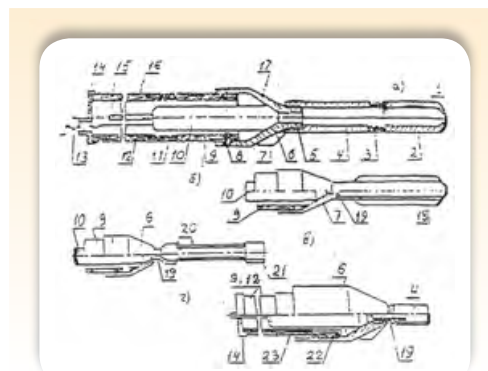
Схемы агрегата и его элементов для разрушения и замены ветхих трубопроводов новыми из полимерных трубных модулей (полиэтиленовых трубных плетей либо отдельных труб, соединяемых сваркой встык оплавлением; а — устройство в сборе; б — направляющая с режущими продольными ножами; в — направляющая с режущими кольцевыми ножами; г — МРр-Рш с упругим элементом и переходной втулкой; 1 — натяжной трос; 2 — головная насадка; 3, 5 — резьба (фрикционное соединение); 4 — концевая насадка; 6 — разрушитель-расширитель; 7 — режущие ножи на разрушителе-расширителе; 8 — пальцы; 9 — первый полимерный модуль; 10 — движитель (пневмоударная машина); 11 — быстро-монтажное соединение; 12 — второй (последующие) полимерные модули; 13 — винтовой домкрат; 14 — упорный фланец (планшайба); 15 — страховочный трос; 16 — шланг для подачи сжатого воздуха; 17 — заходная часть разрушителя-расширителя; 18 — продольные режущие ножи; 19 — переходной элемент; 20 — тяги; 21 — кольцевые режущие ножи; 22 — упругий элемент; 23 — переходная втулка)
